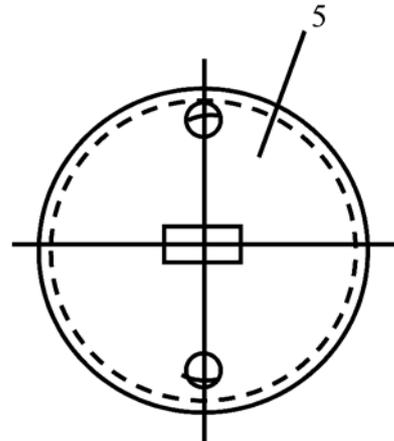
Установочная пластина рупорной приставки (вид спереди)
